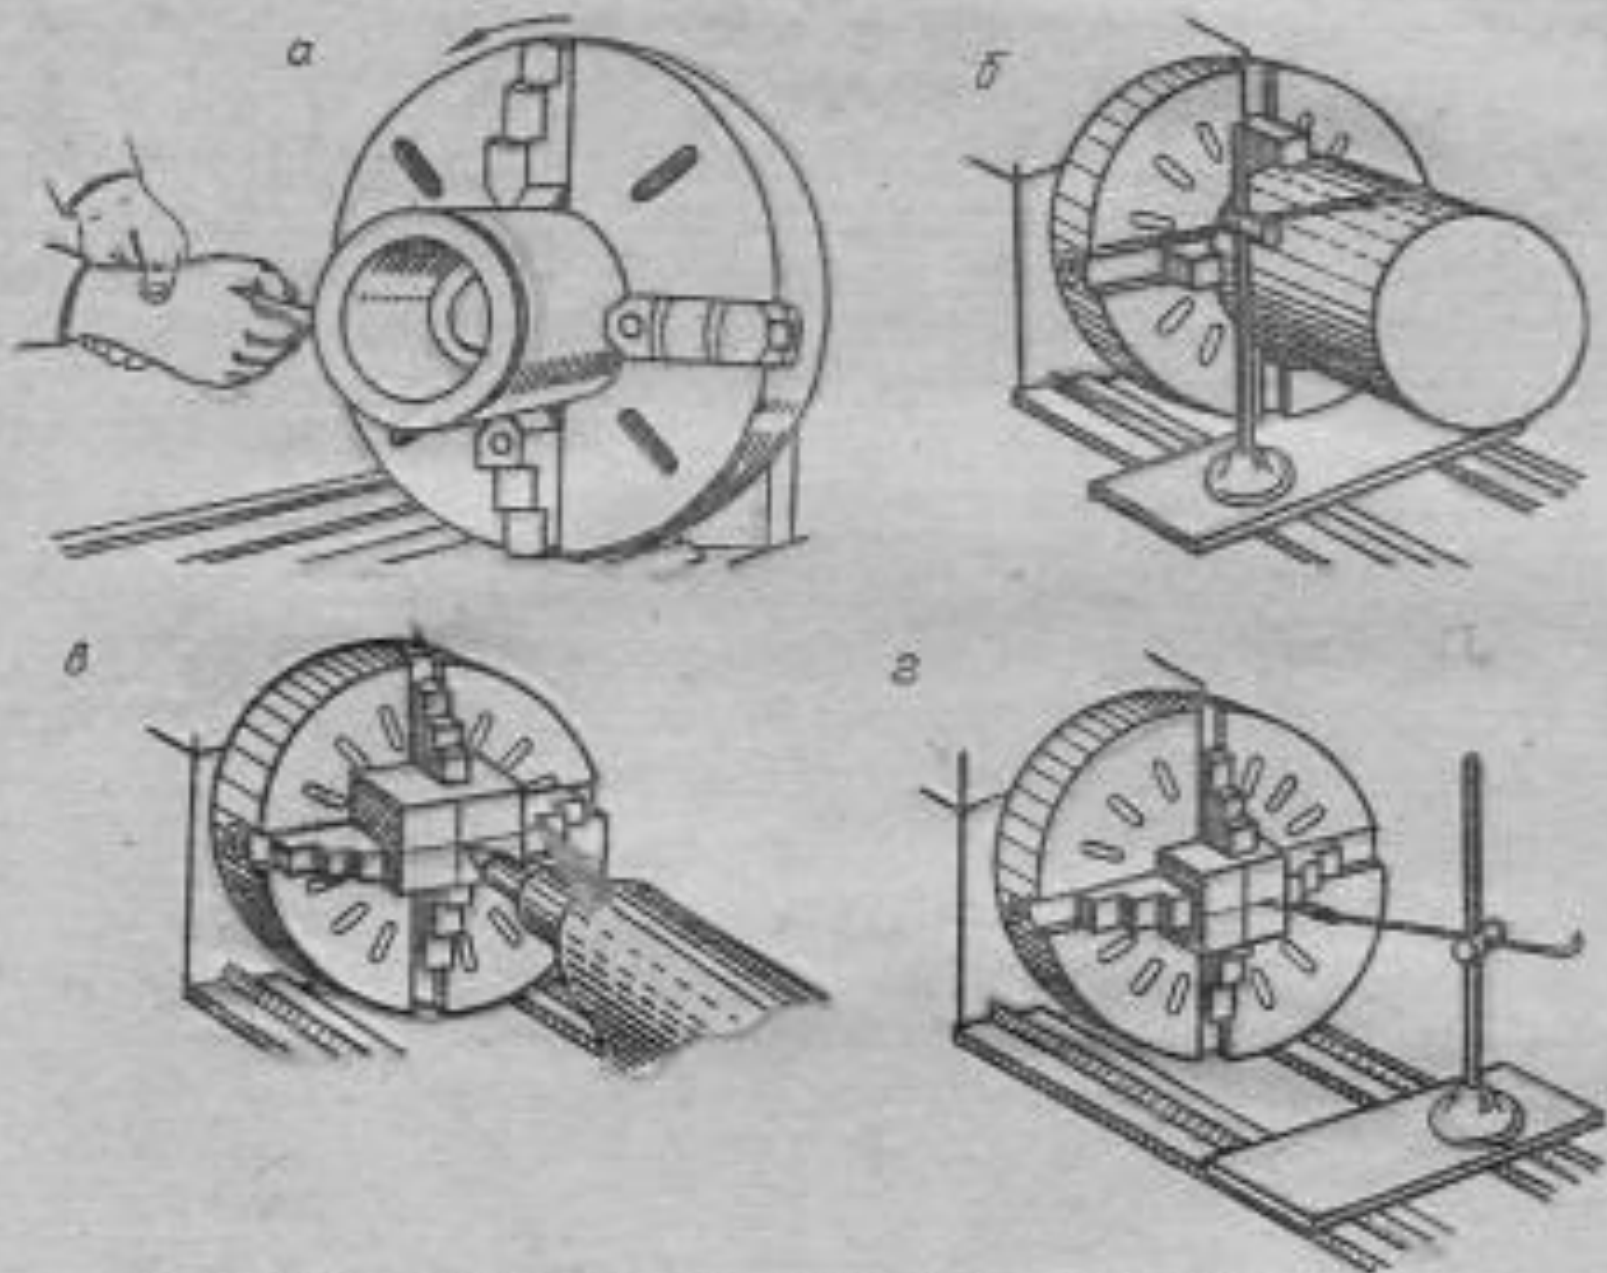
Способы выверки заготовок в 4-кулачковом патроне.
